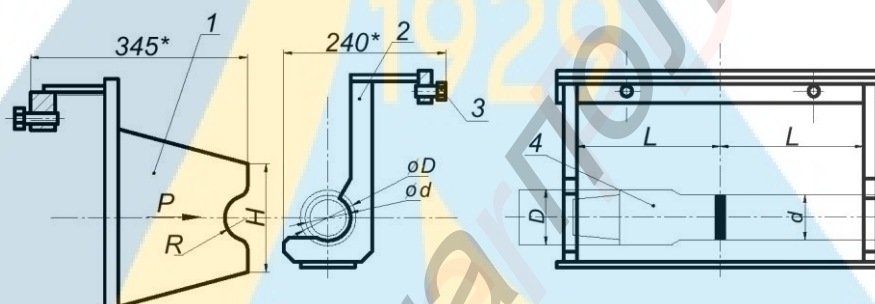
Приставка до розривної машини Дніпропетровського заводу бурового устаткування для випробування труб на вигин: 1 - упор; 2 - опора; 3 - болти; 4 - випробовуваний зразок зварного шва
